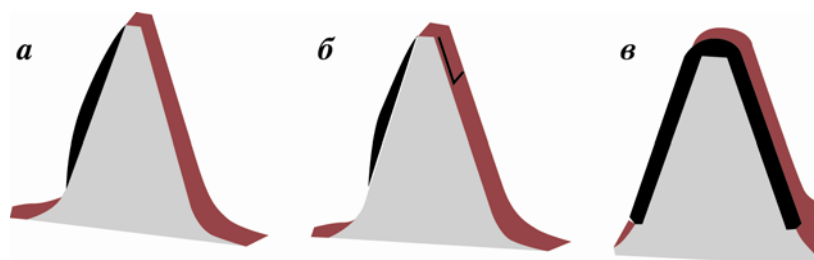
Типовые формы фрезерованных зубцов шарошечных долот производства ОАО «Волгабурмаш»:
